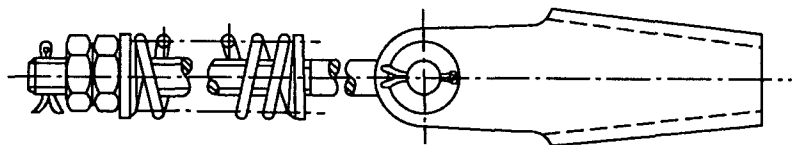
Устройство подвески с цилиндрической пружиной
